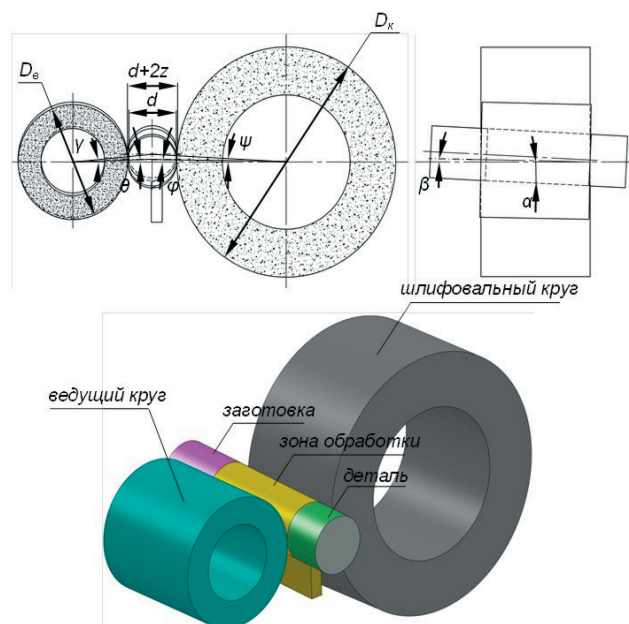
Схема бесцентрового шлифования со скрещивающимися осями инструмента и детали
